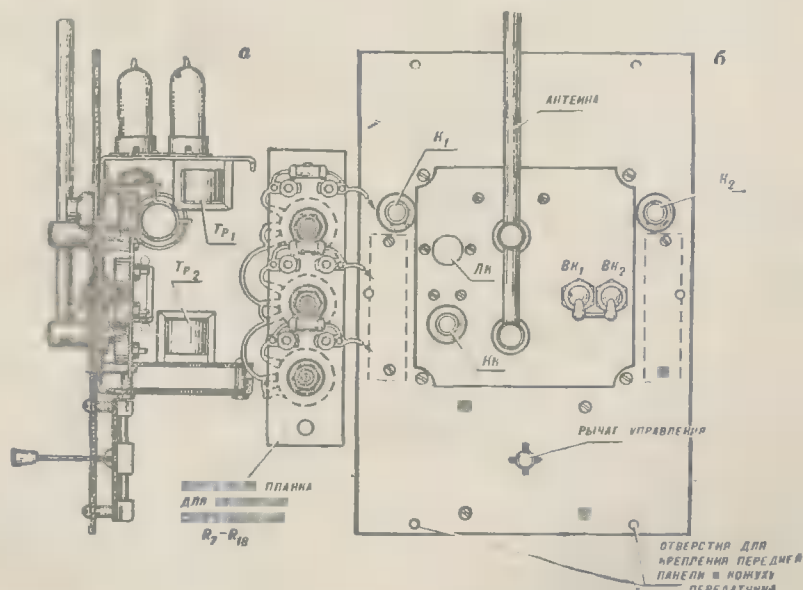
Сборочный чертеж передатчика: а — вид сбоку; б — вид спереди.
